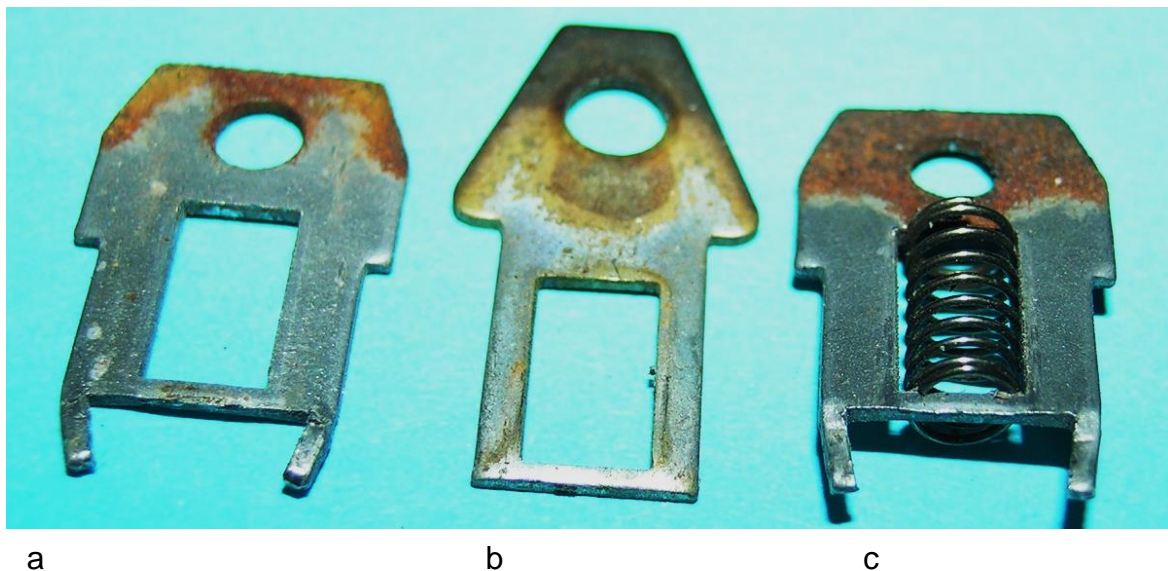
Einzelteile der Kabelanschlussklemme: a) Außenblech, b) Mittelblech, c) Zweites Außenblech mit der Schraubenfeder
